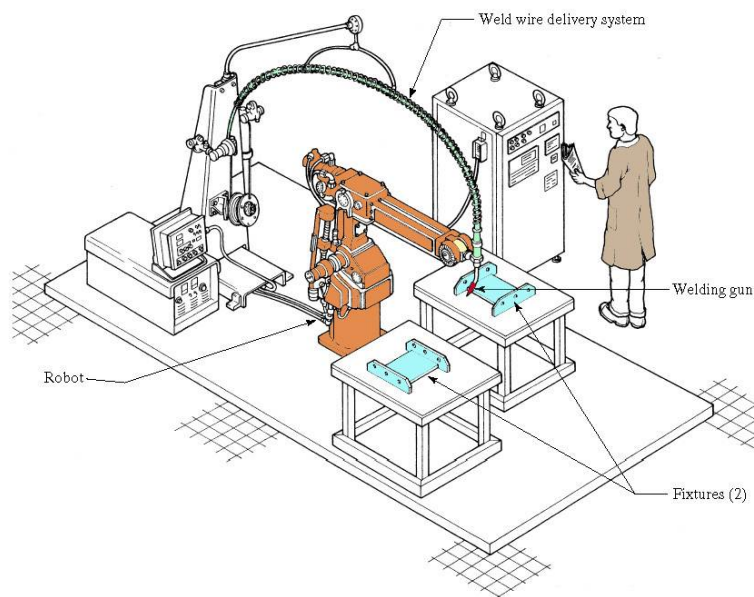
Celda de trabajo para soldadura por arco eléctrico robotizada. Fuente [32].
